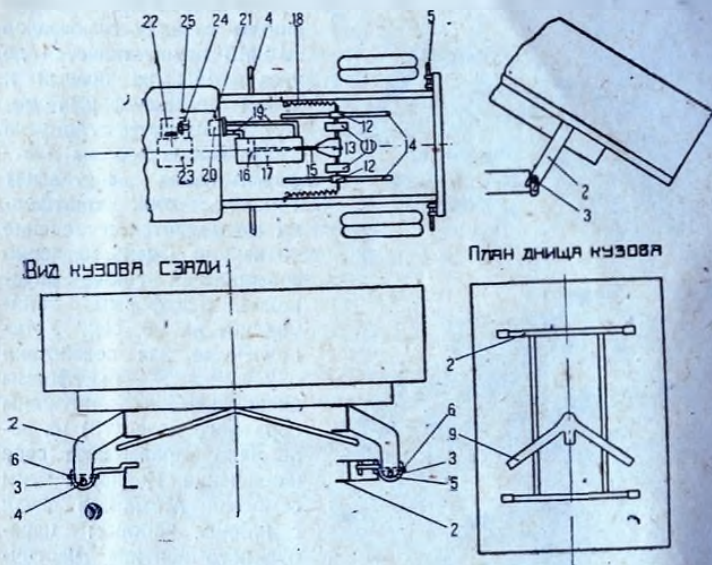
Общий вид гидравлического самосвала „ВУД“ нового типа.
